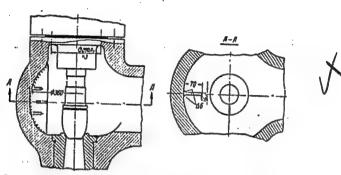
Установка внарного разделителя в паровой коробке клапана.
